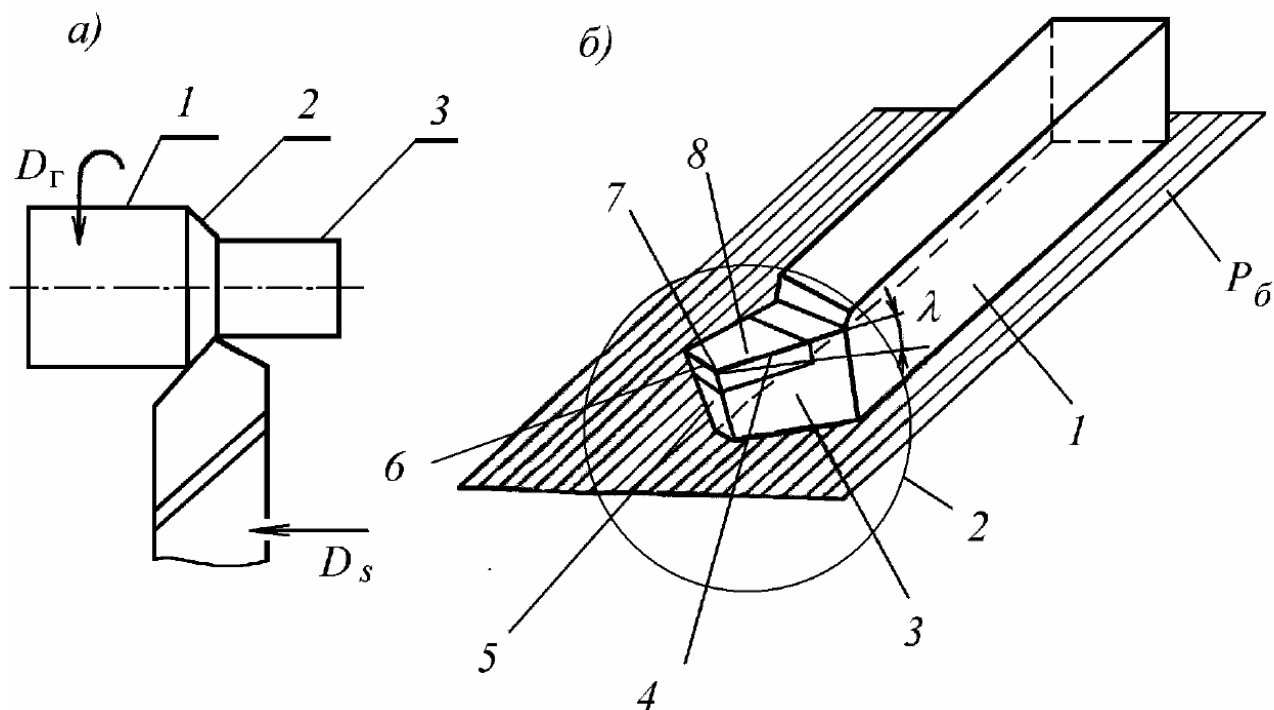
Схема точения (а), токарный проходной резец (б)
